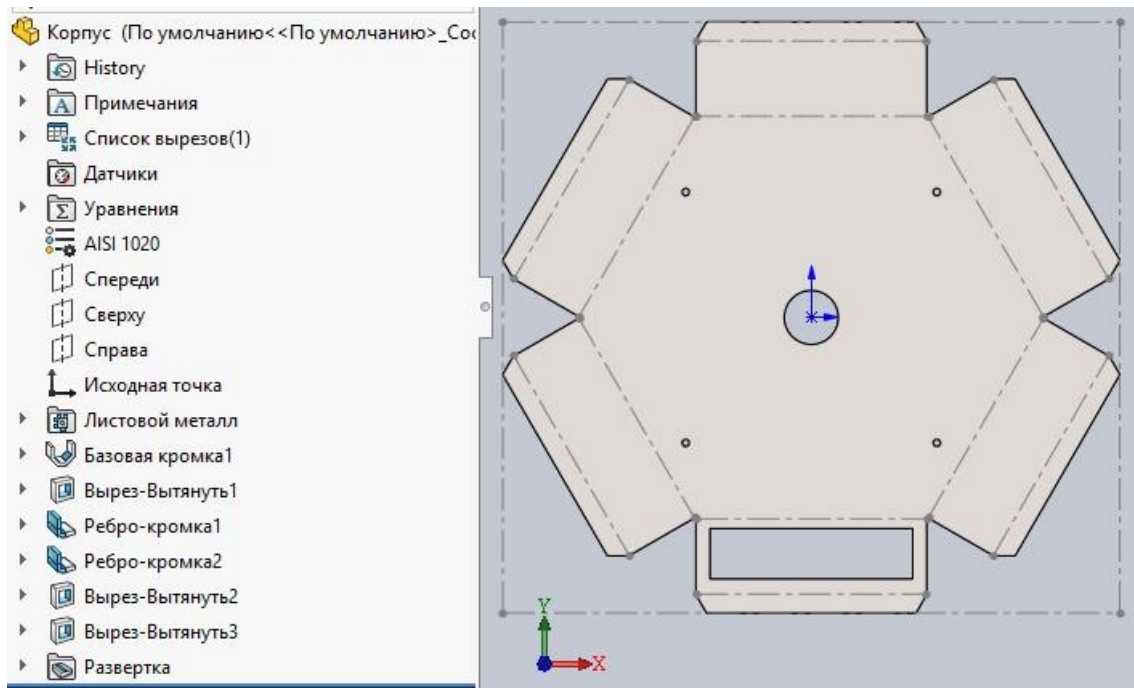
Розгортка корпусу ротаційного подрібнювача
